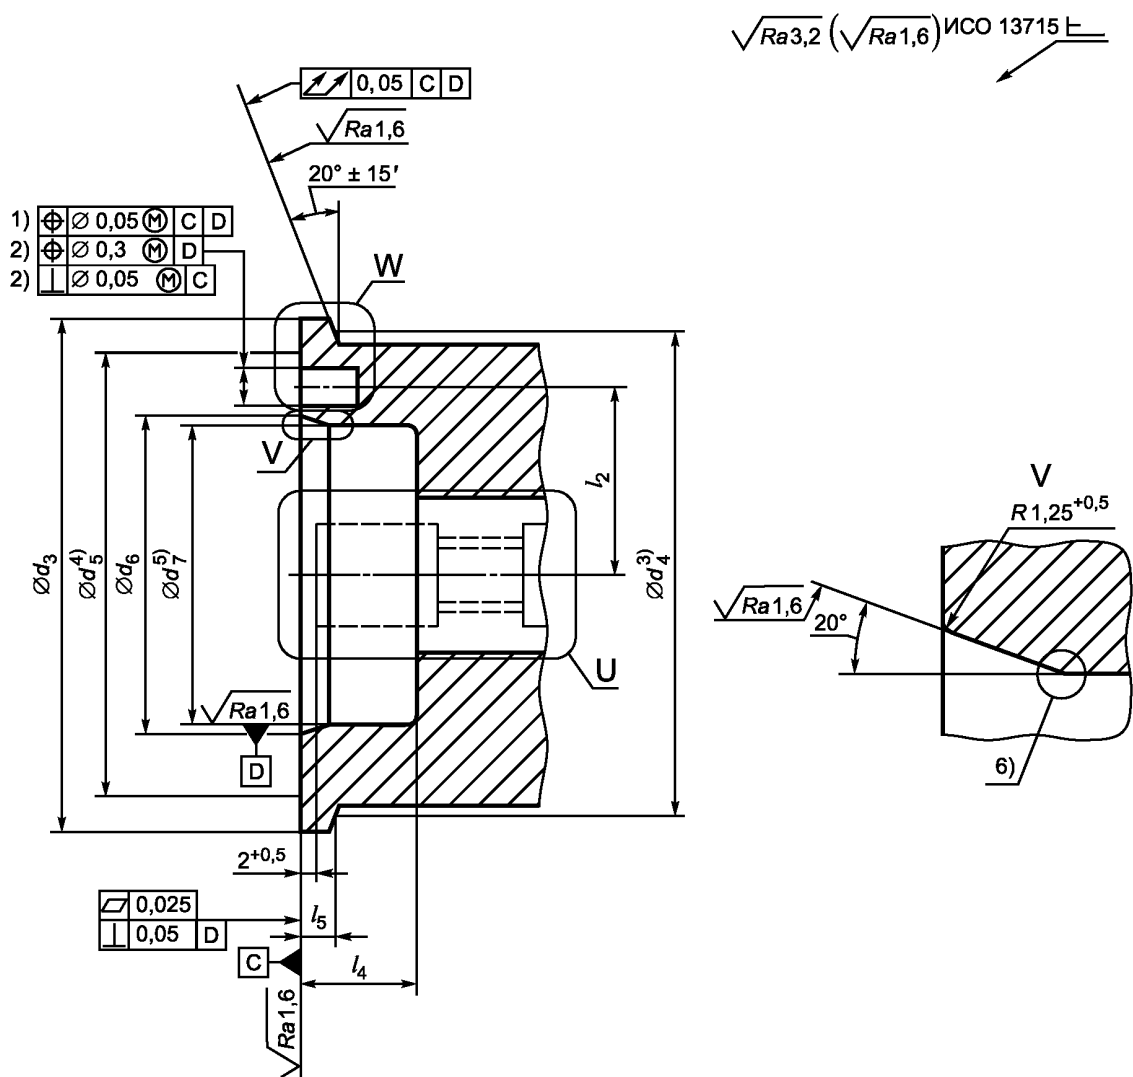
Конструкция и размеры фланцев приводов агрегатов и фланцев двигателя/редуктора (лист 1)
